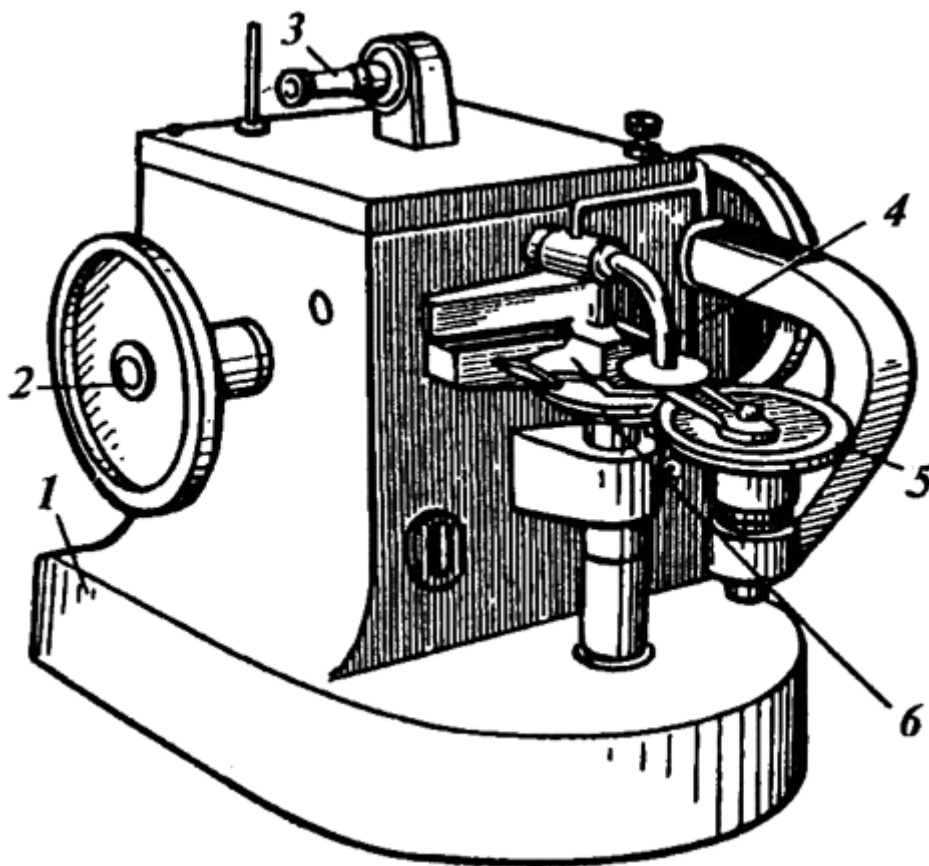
Скорняжная швейная машина кл.10-Б: 1 - корпус; 2 - главный вал; 3 - механизм регулирования натяжения нитки; 4 - петлитель; 5 - нажимной диск; 6 - ведущий диск
